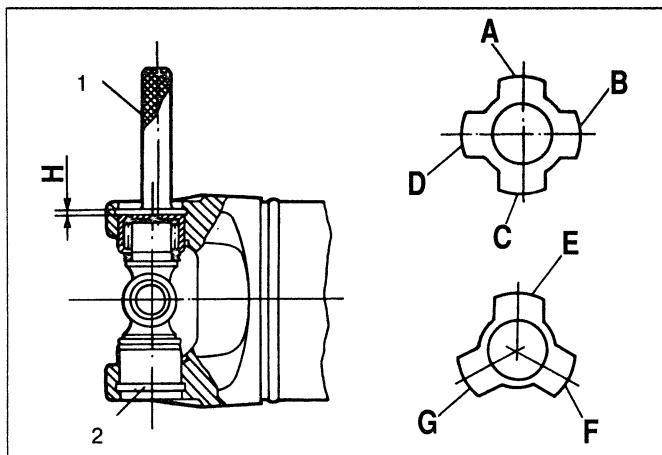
Сборка карданного шарнира: 1 – стопорное кольцо; 2 – калибр; Н – зазор; А, В, С, D, E, F, G – лепестки калибров, имеющие толщину, мм: 1,45; 1,48; 1,52; 1,56; 1,60; 1,64; 1,67
